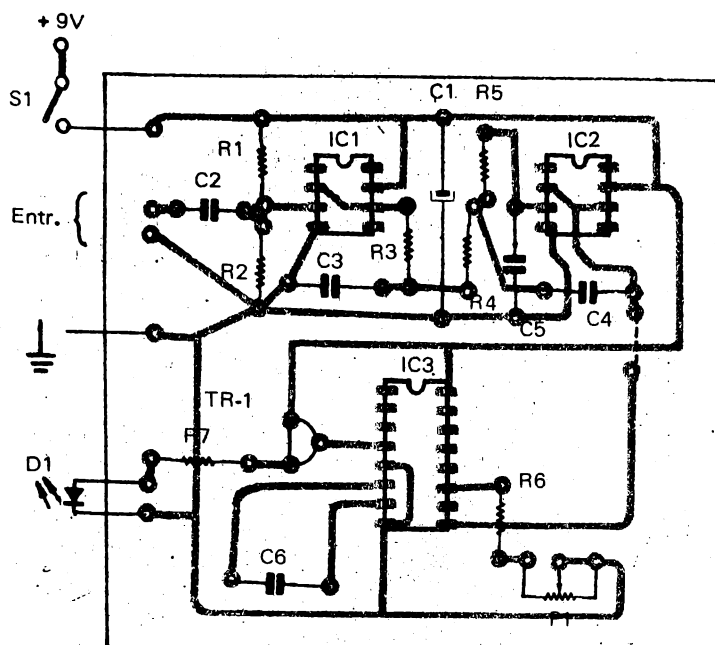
Disposición de componentes sobre el impreso del emisor.
